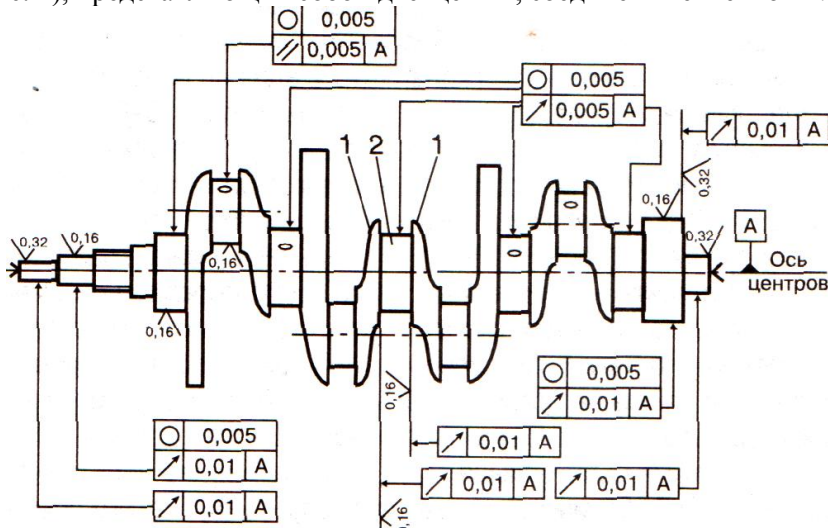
Схема и основные требования к качеству и расположению поверхностей коленчатого вала: 1 — щека; 2 — шейка
